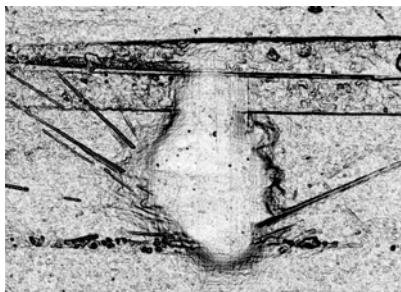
Фотография вихревого облака аэрозоля над областью сварки
